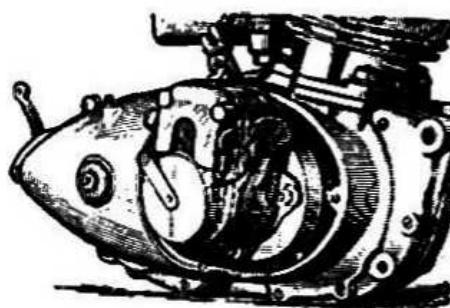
Общий вид установки магнито на двигатель ИЖ-49
